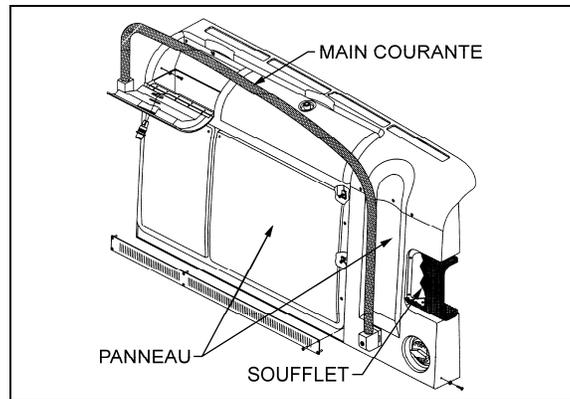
EMBLEMMENT DES PANNEAUX
